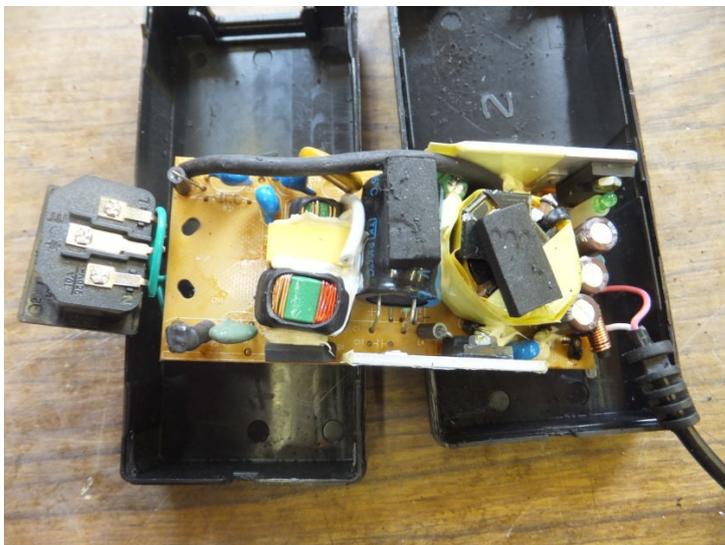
, das aufsägen des verschweissten Gehäuse
